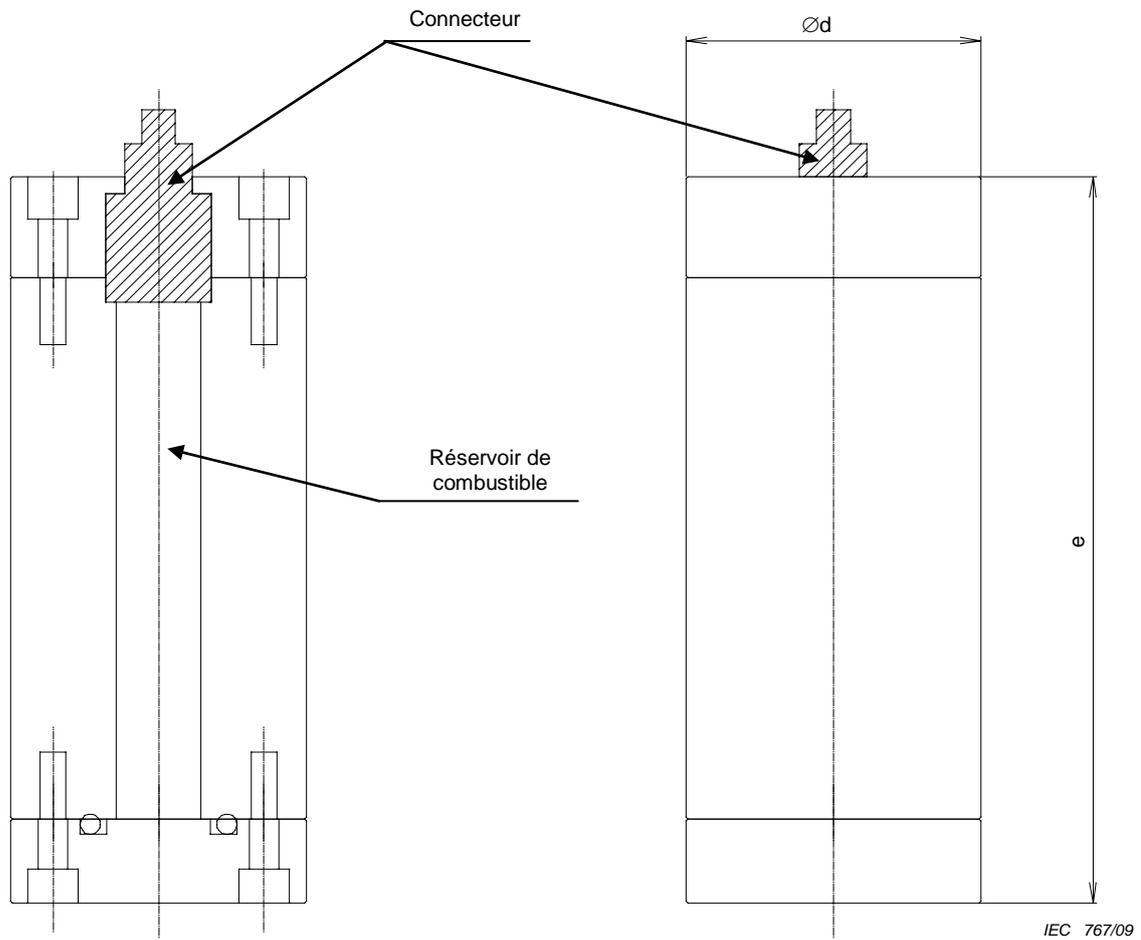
Dispositif d'essai de l'appareil pour les essais des cartouches de 4.4.9
